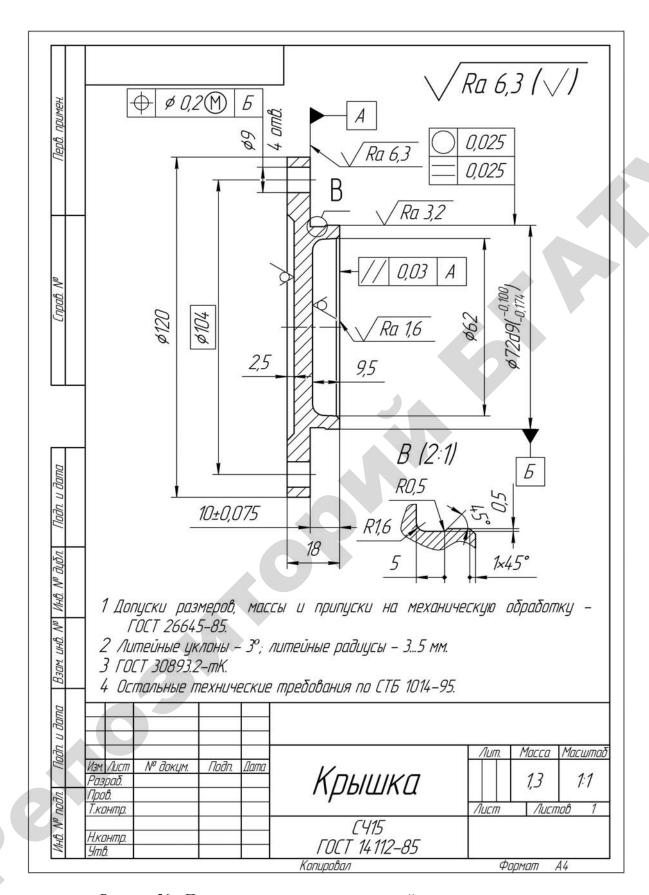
Пример выполнения чертежа глухой крышки подшипника
